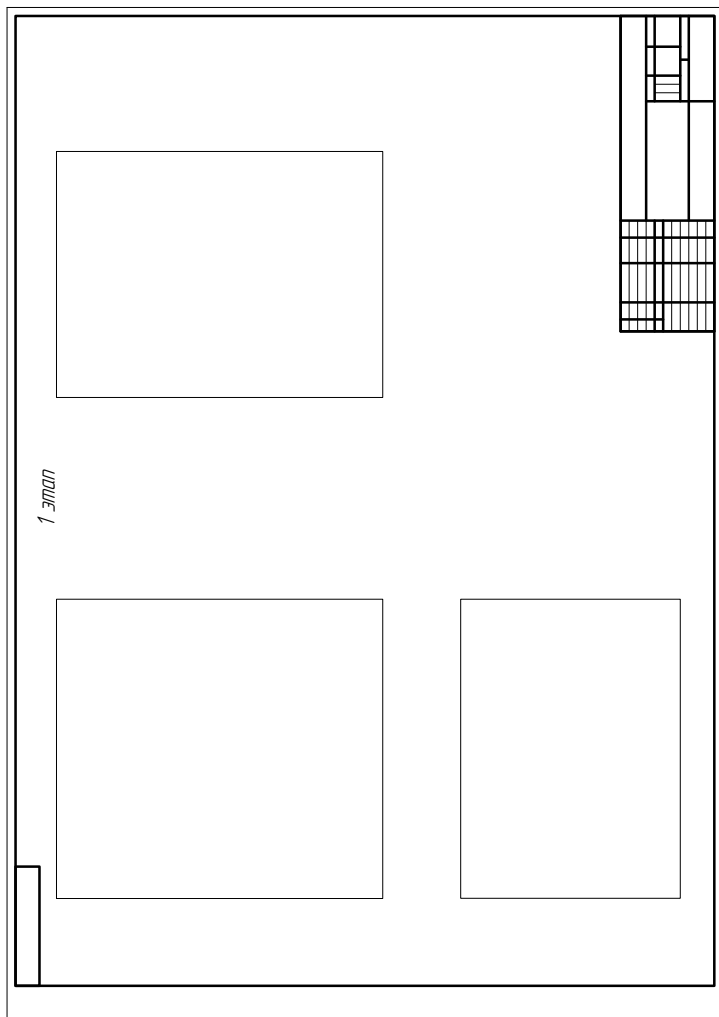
Размещение изображений сборочной единицы по габаритным размерам
